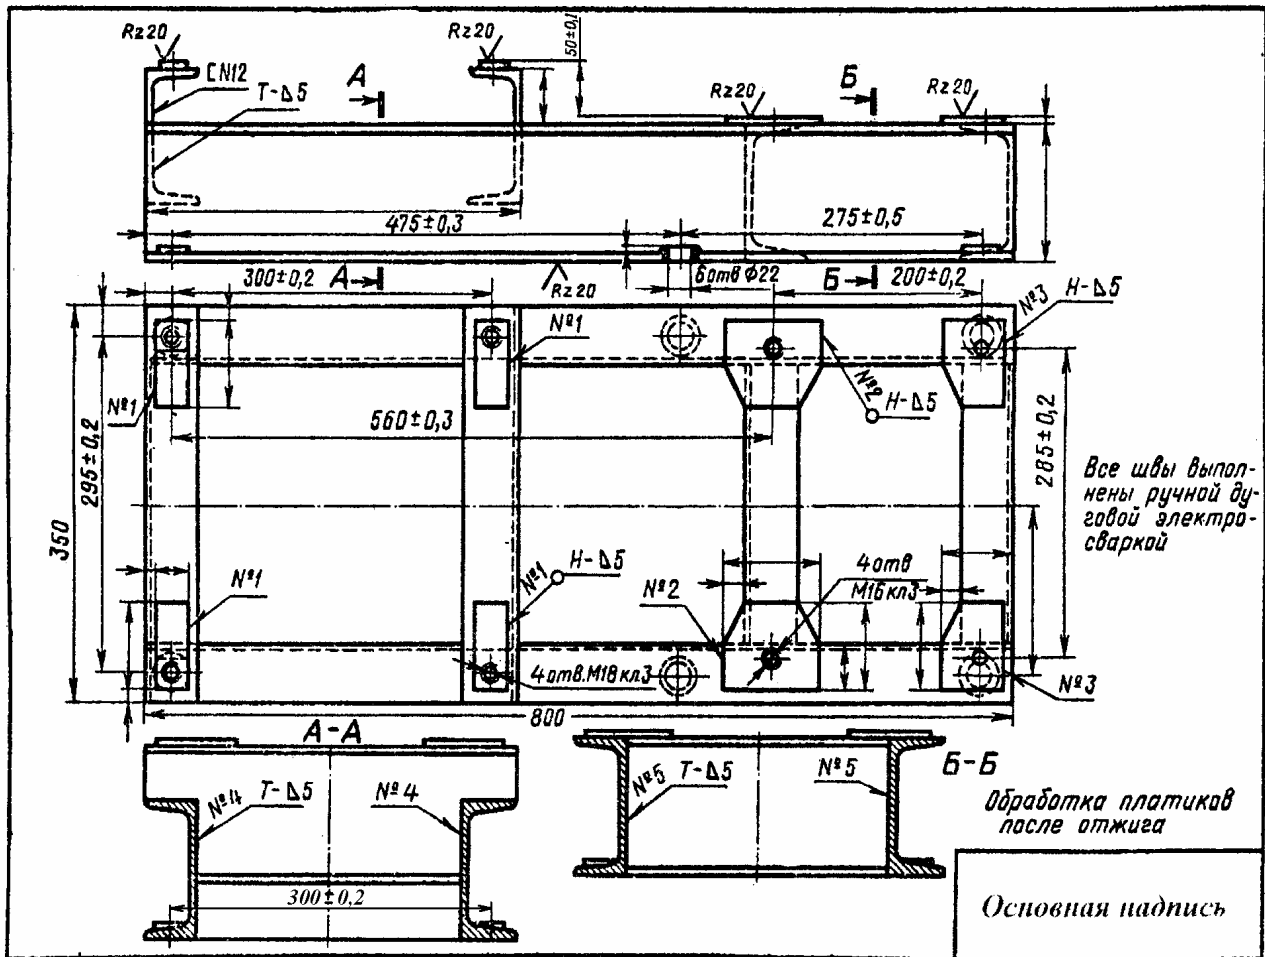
Рабочий чертеж сварной рамы
